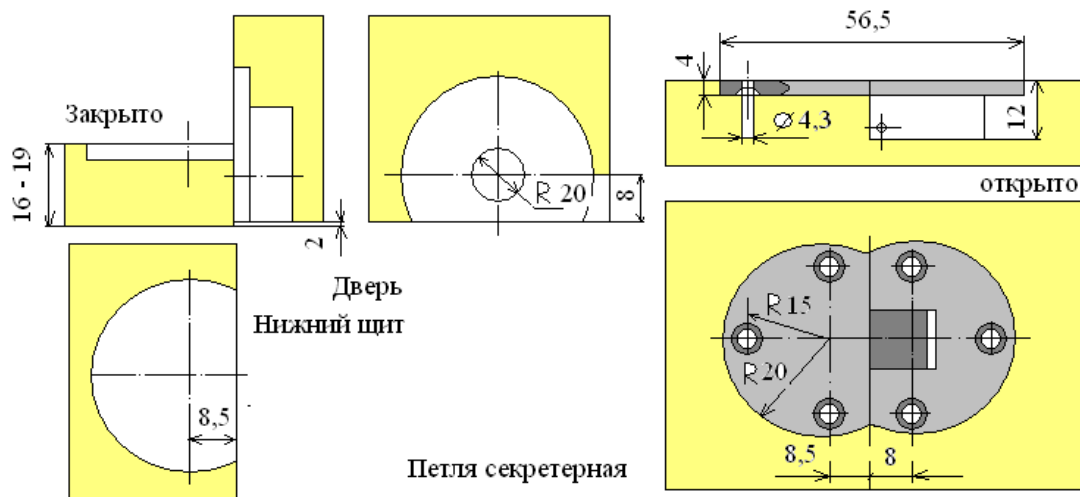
Установка откидных дверок секретера на специальные петли
